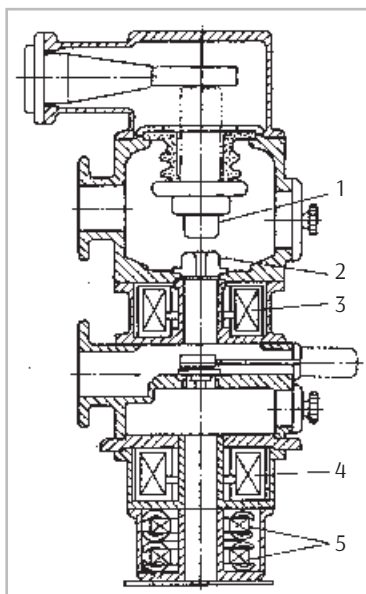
Схема конструкции типовой сварочной ЭЛП: 1 — катодный блок; 2 — анодный блок; 3, 4 — фокусирующие линзы; 5 — обмотка
